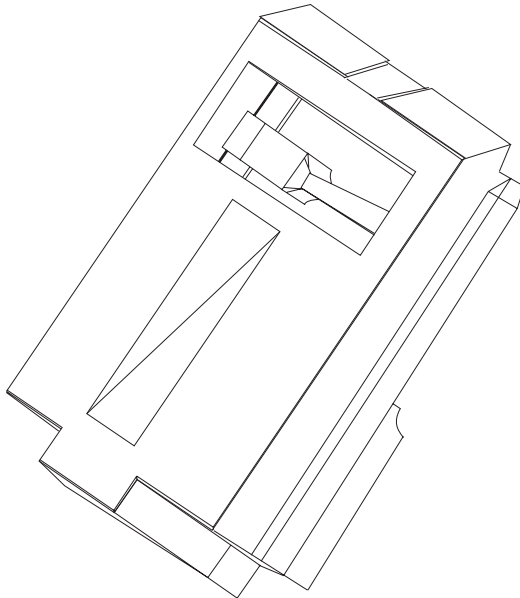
Schieber für die Montage des TS Adapter IE auf einer Hutschiene
